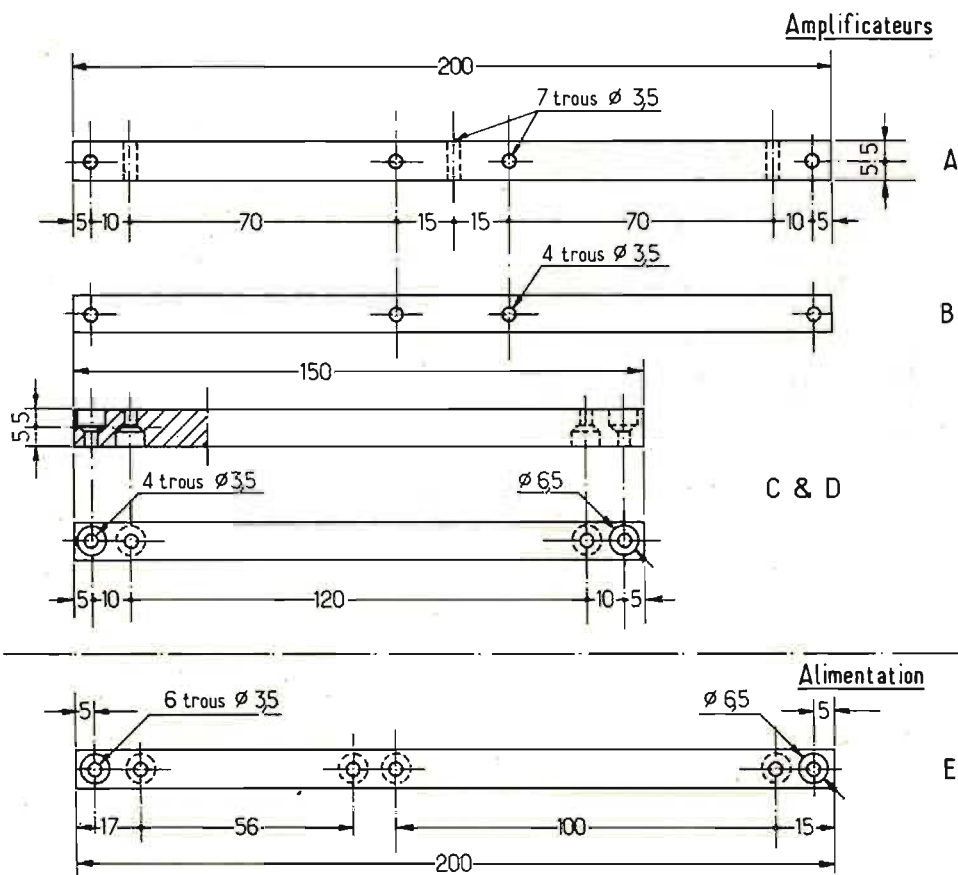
Barres de fixation (A65 ou Dural, section 10 x 10 mm).
